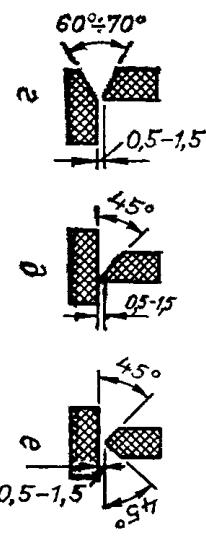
Подготовка кромок деталей перед сваркой горячим газом:
